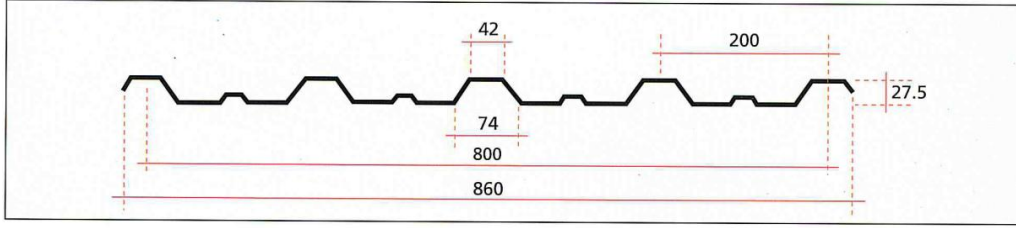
Trapez oluklu plağın 3. bükümü.
